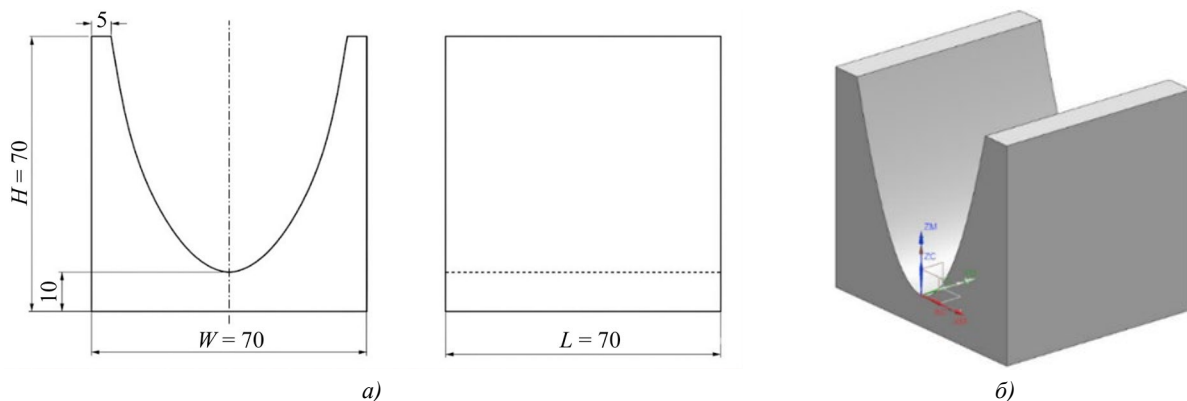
Чертеж экспериментального образца *a* — двухмерный чертеж; *б* — трехмерная модель
